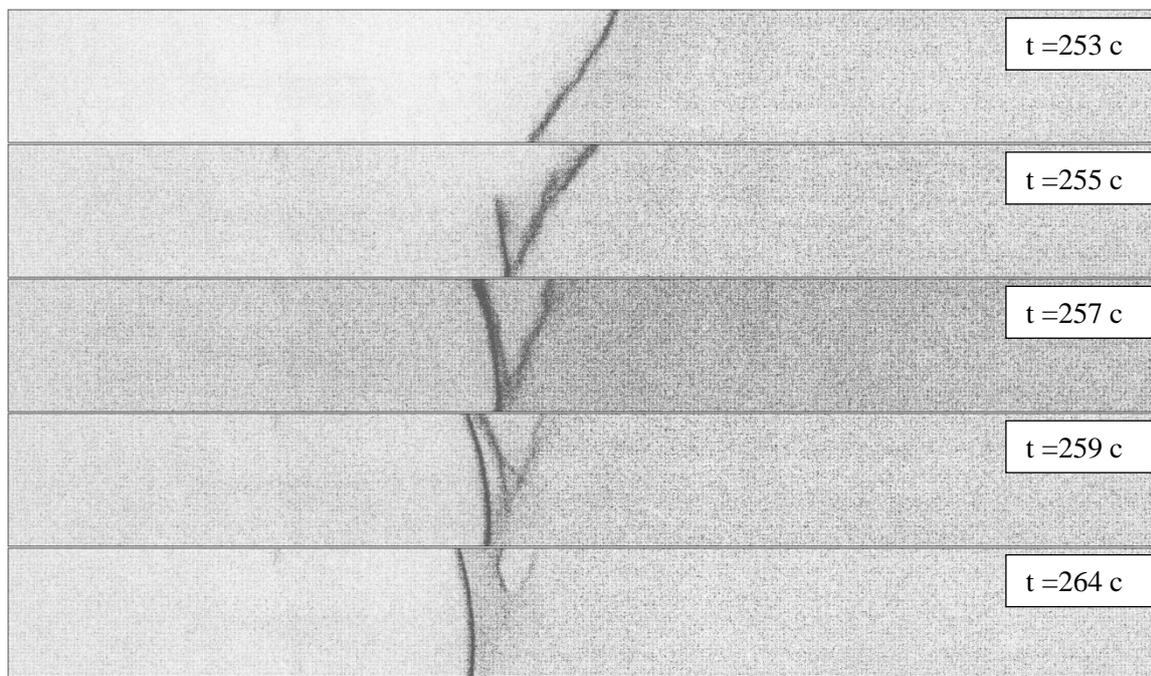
Поведение полос Чернова-Людерса в зонах сварного соединения
